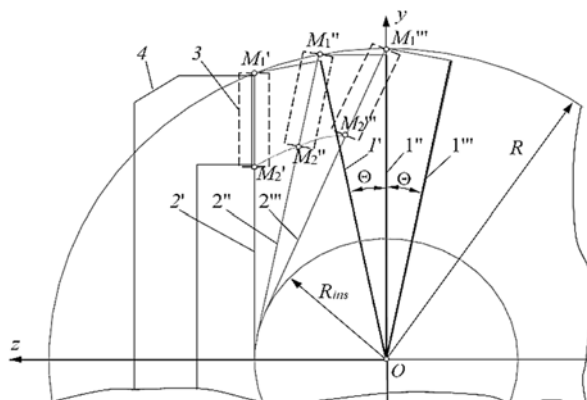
Схема взаимодействия ролика и зубчатого колеса: 1 – сателлит; 2 – ось ролика; 3 – профиль ролика (фрезы); 4 – колесо
